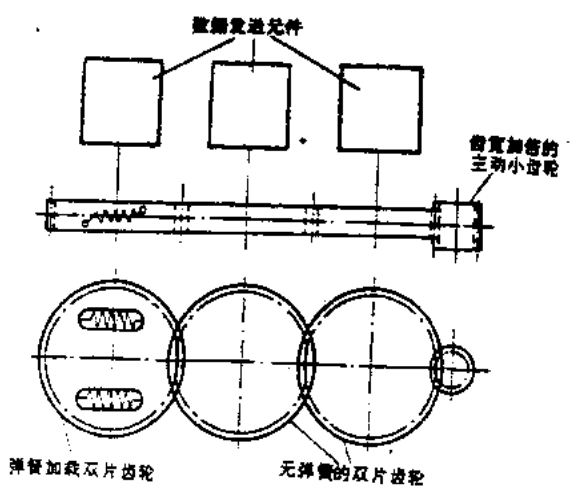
双片齿轮轮系加一个弹簧加载双片齿轮
